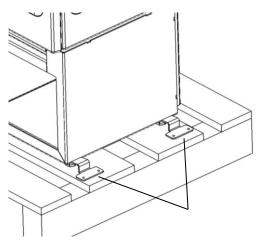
Detalle de las chapas que amarran las patas a la base de madera
